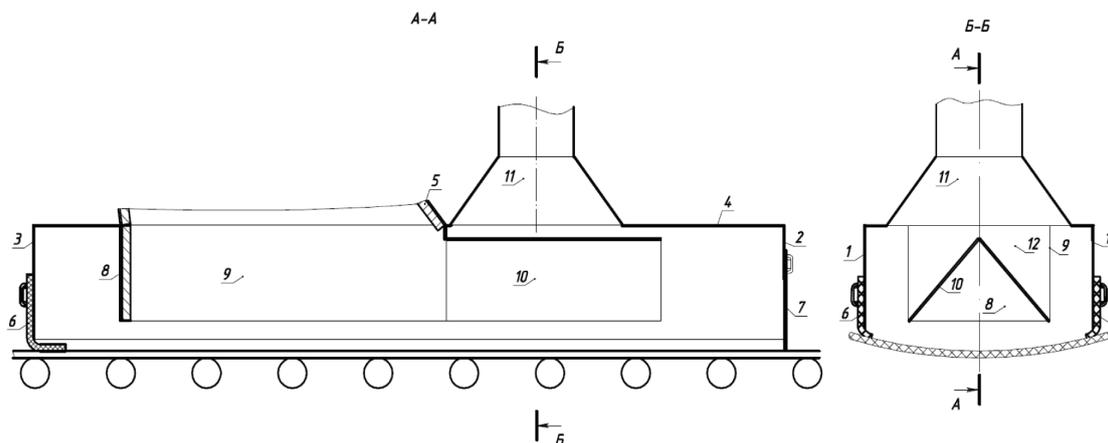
Аспирационное укрытие мест перегрузки сыпучих материалов [2]: 1 – верхняя крышка; 2, 3, 4 – задняя, передняя и боковые стенки; 5 – перегрузочный желоб; 6, 7 – эластичные уплотнения; 8 – задняя стенка внутреннего короба; 9 – боковые стенки внутреннего короба; 10 – боковые наклонные стенки внутреннего короба; 11 – аспирационная воронка; 12 – передняя стенка внутреннего короба.
